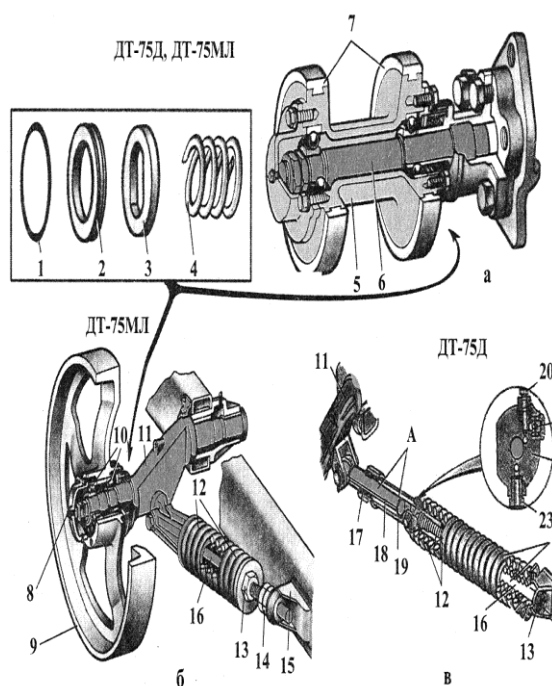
Підтримуючий ролик (а), механічний (б) і гідравлічний (в) натяжні механізми: 1 – гума рухомого кільця; 2, 3 – рухоме і нерухоме ущільнюючі кільця; 4 – пружина; 5 – маточина; 6 – вісь; 7 – гумовий бандаж; 8 – пробка заливного і контролюючого отвіра; 9 – напрямне колесо; 10 – роликові конічні підшипники; 11 – колінчаста вісь; 12 – амортизуючі пружини; 13 – гайка тиску пружин; 14 – регулювальна гайка; 15 – кронштейн рами; 16, 20 – стяжний і замковий гвинти; 17 – ущільнююча манжета; 18 – шток; 19 – циліндр натягування гусениці; 21 – прес-маслянка; 22 – головка циліндра; 23 – запобіжний клапан; А – пристрій гідравлічного натягування; Б – пружинний амортизатор.
